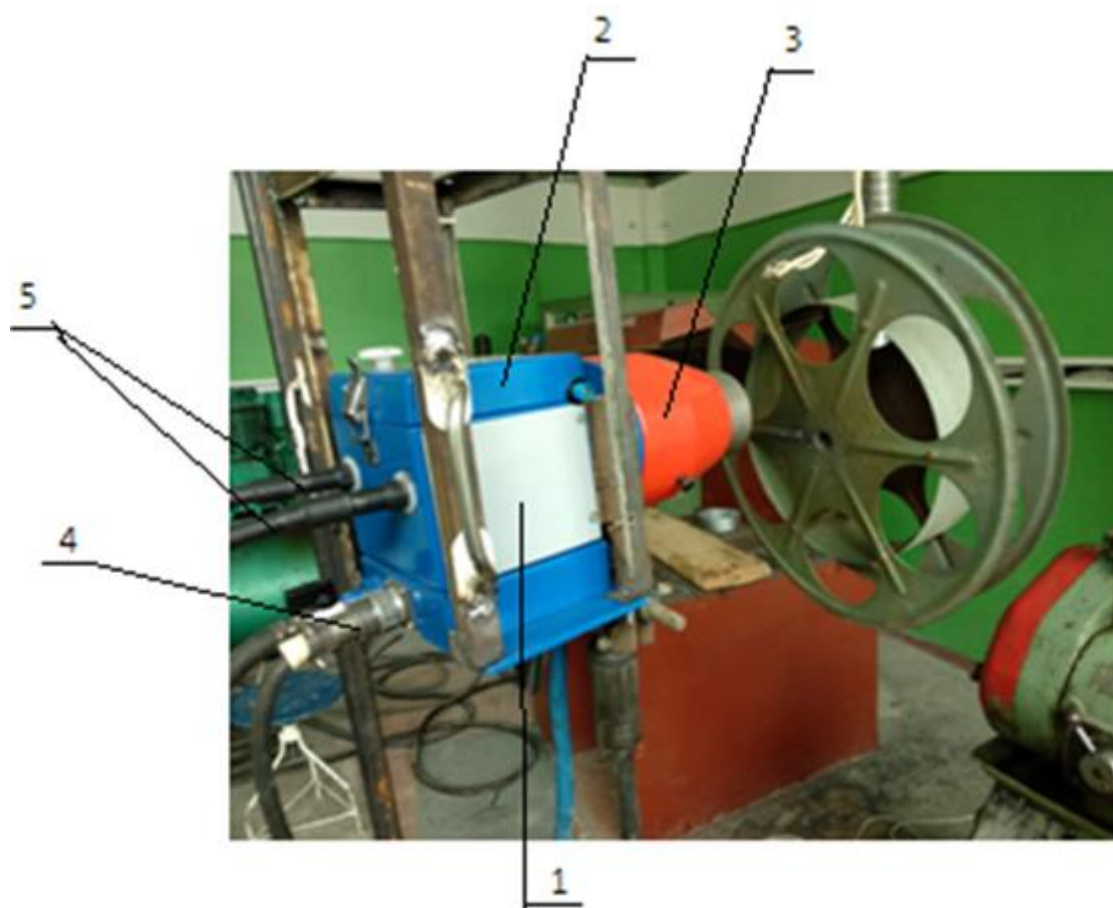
Фотография общего вида металлизатора ЭДМ-11ШД
